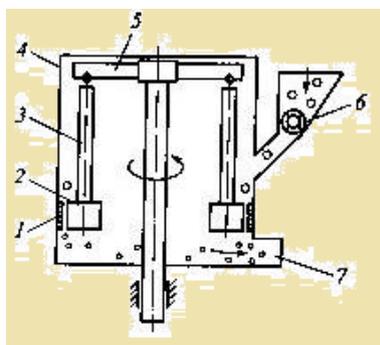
Маятниковая мельница: 1 – кольцо; 2 – ролик; 3 – маятник; 4 – корпус; 5 – крестовина; 6 – питатель; 7 – пневмотранспортная труба
